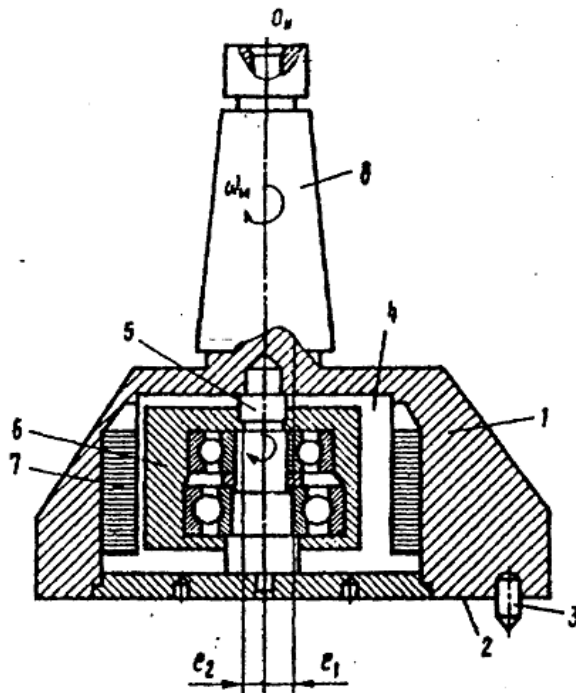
Торцева фреза з ексцентрично розташованим ротором [41]
